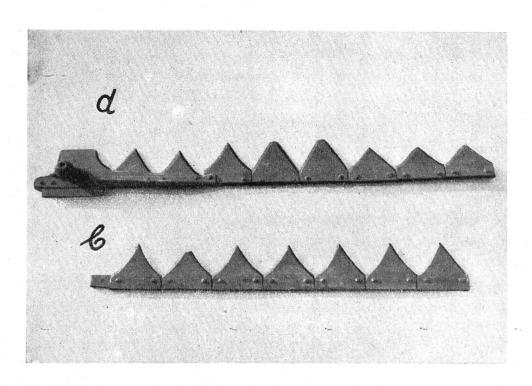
a) Ces sections ont été utilisées beaucoup trop longtemps. Avec de telles sections une bonne coupe n'est pas possible.
